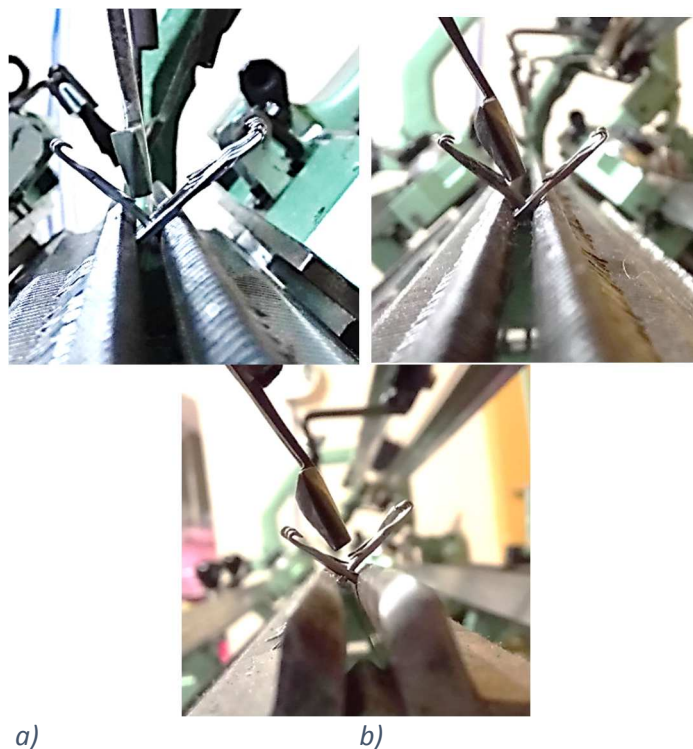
a) Posición de la punta del guía hilo sobre las agujas al extremo izquierdo de la máquina
